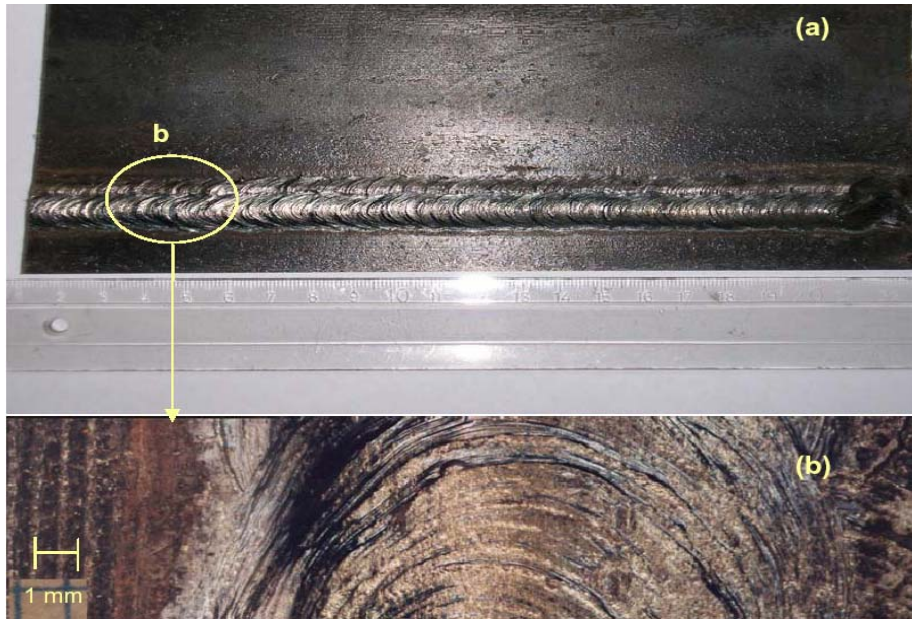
Cordón de soldadura: (a) Vista general; (b) Detalles de los rizos.
